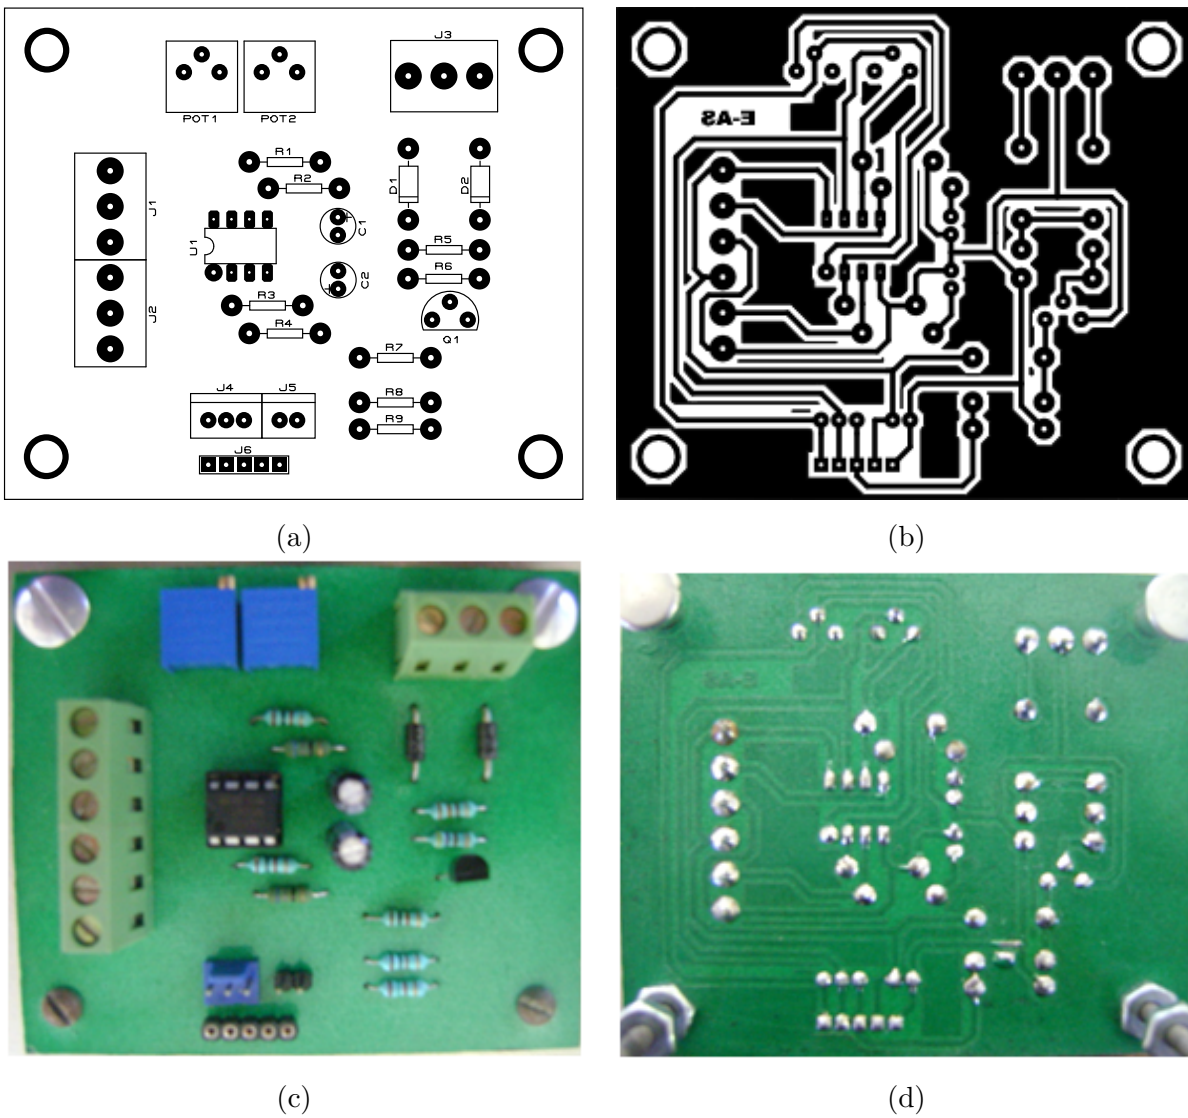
(a) Vista Superior del PCB. (b) Vista Inferior del PCB. (c) Vista Superior del PCB real. (d) Vista Inferior del PCB real.
